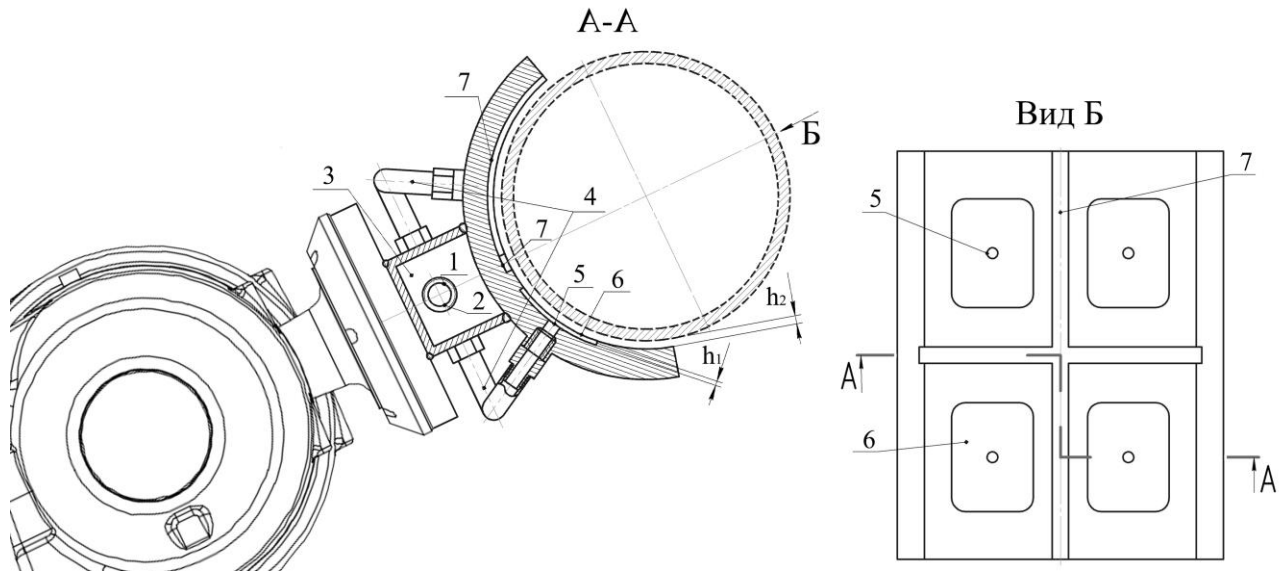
Безконтактний струминний захоплювальний пристрій
